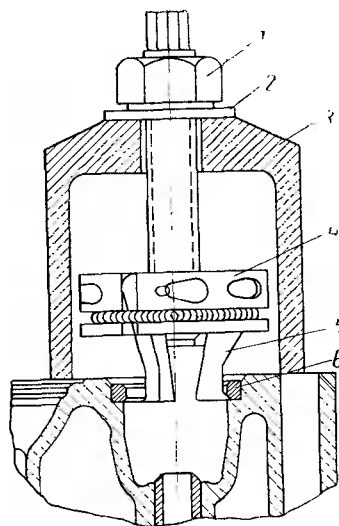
Приспособление для выпрессовки седел выпускных клапанов:
